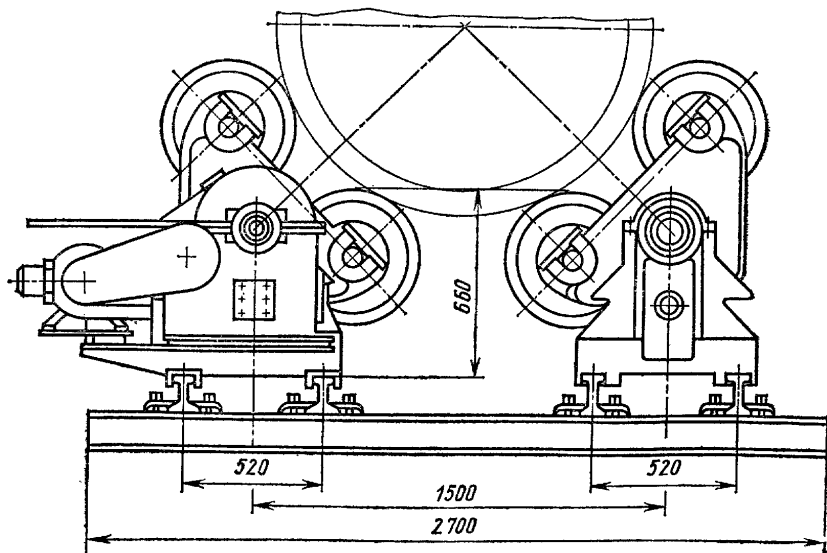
Роликовый стэнд с балансирными ролюкоопорами
